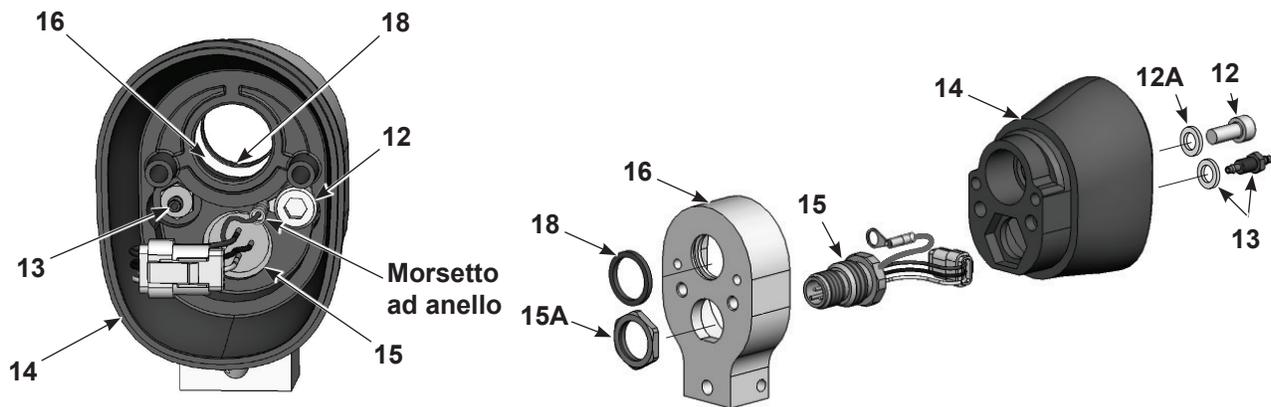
Smontaggio della pistola con montaggio su barra 3 di 3
